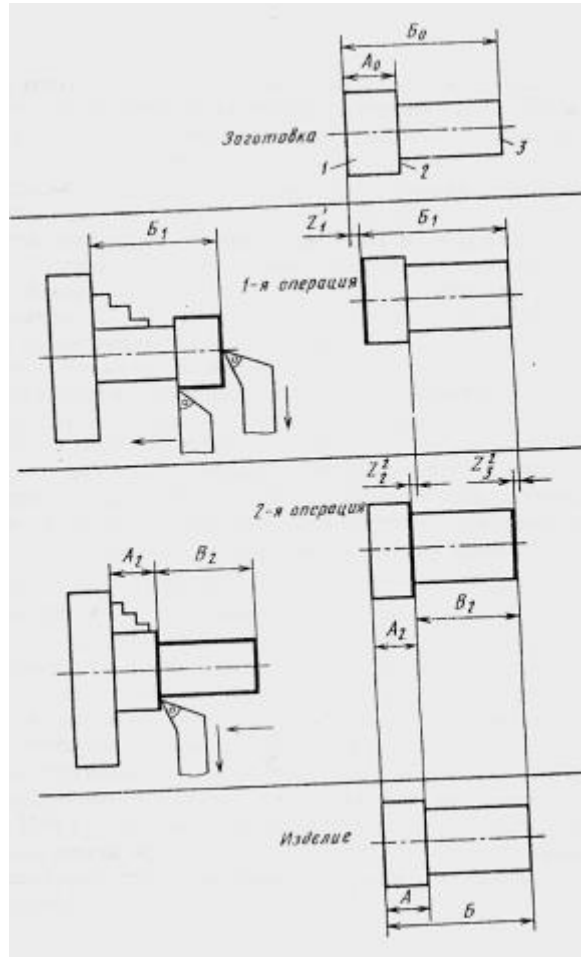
Схема преобразования размеров заготовки в процессе изготовления детали
